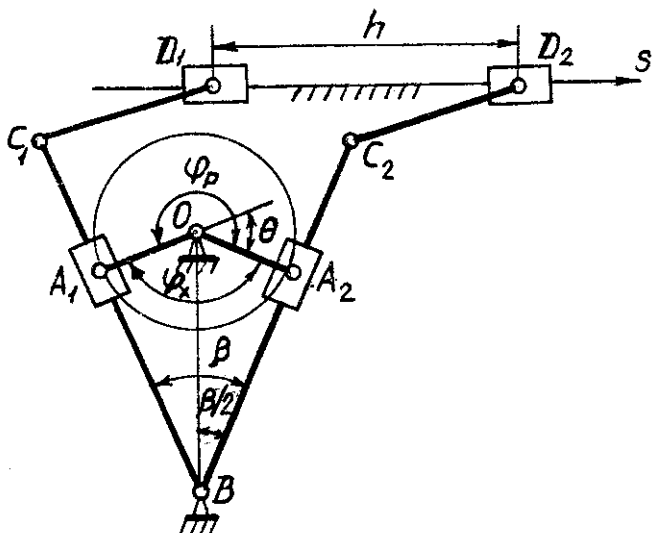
Шестизвенный кулисный механизм строгального станка
